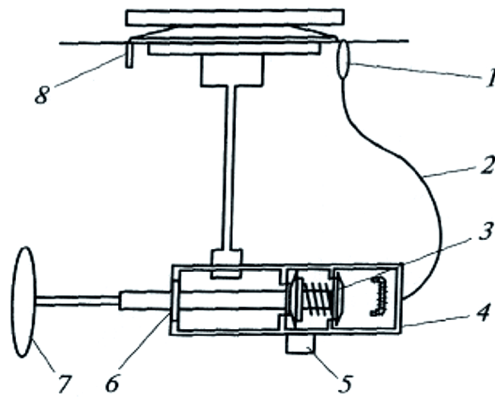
Схема автоматики безопасности газового контроля: 1 — датчик пламени; 2 — термопара; 3 — пружина; 4 — электромагнит; 5 — подача газа; 6 — кран; 7 — рукоятка; 8 — свеча электророзжига
